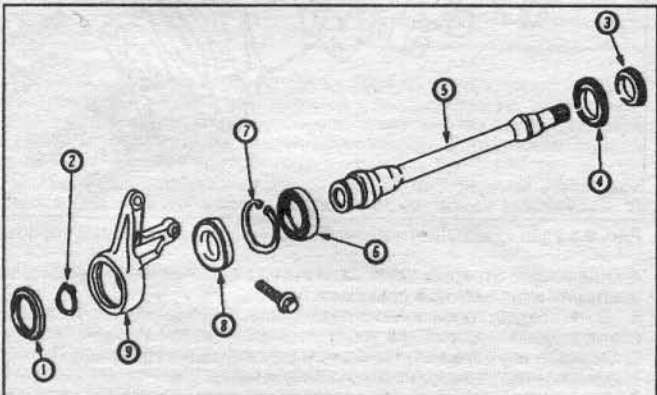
Сборка промежуточного вала и опоры подшипника: 1 - внешний сальник; 2 - внешнее стопорное кольцо; 3 - кольцо промежуточного вала; 4 - кольцо опоры; 5 - промежуточный вал; 6 - внутренний сальник; 7 - внутреннее стопорное кольцо; 8 - подшипник промежуточного вала; 9 - опора.
